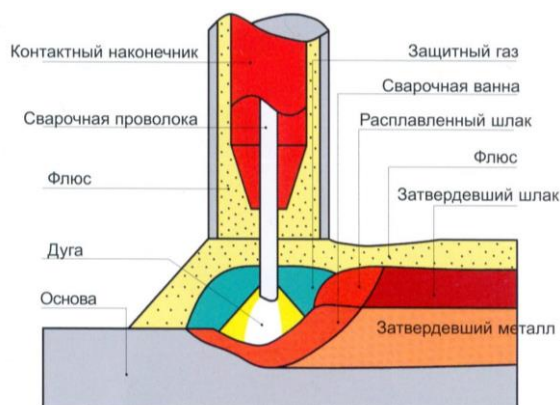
Схема выполнения сварки под флюсом
